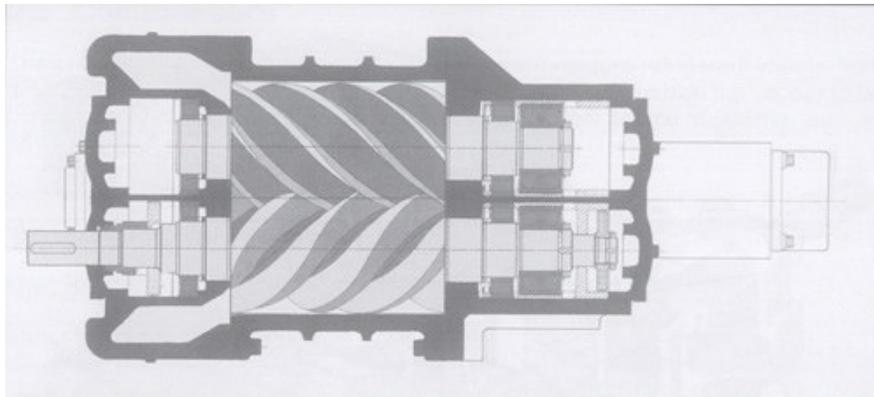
Esquema de compresor de doble tornillo rotativo.
